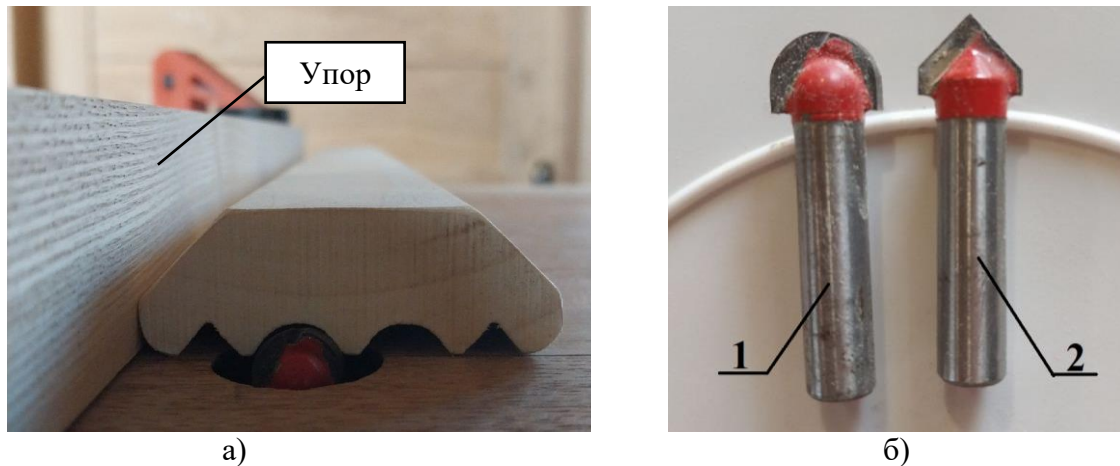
Виготовлення профілю плінтуса фрезеруванням а) та використані фрези б)
